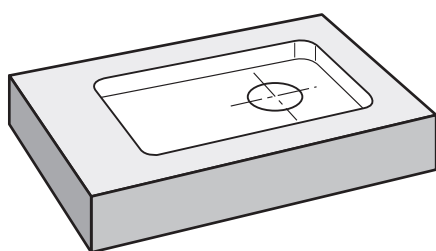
Образцовая деталь – Изготовление прямоугольного кармана
